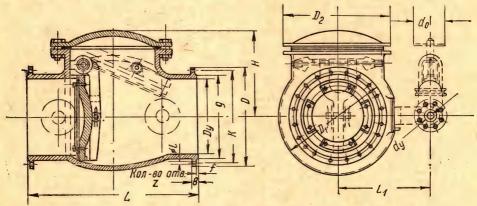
Клапан обратный поворотный 19ч16бр.
